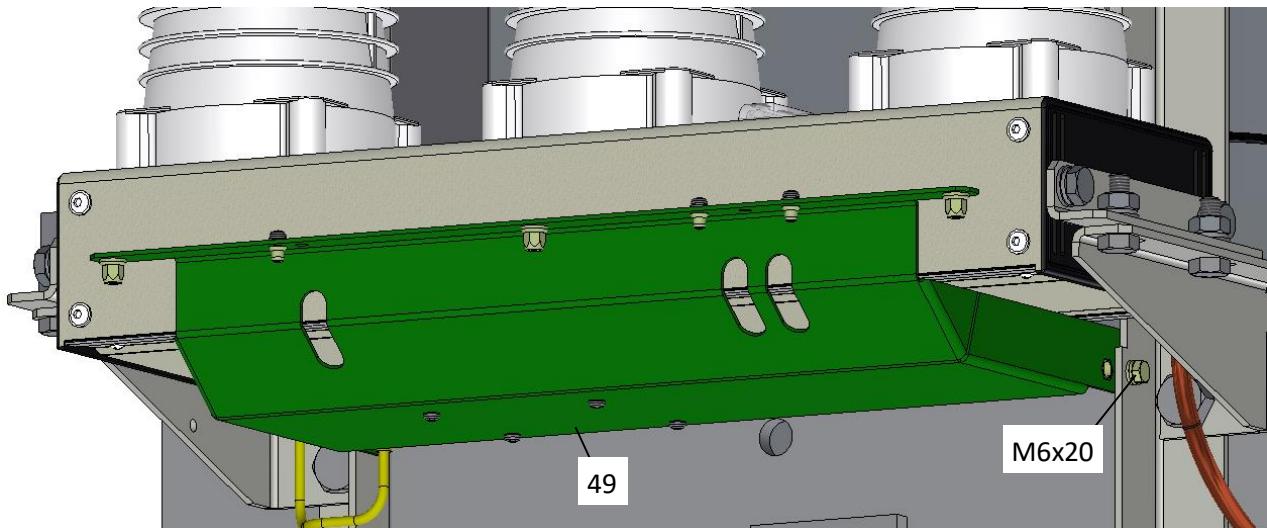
Установка крышки с платой сопряжения на ВЭ
